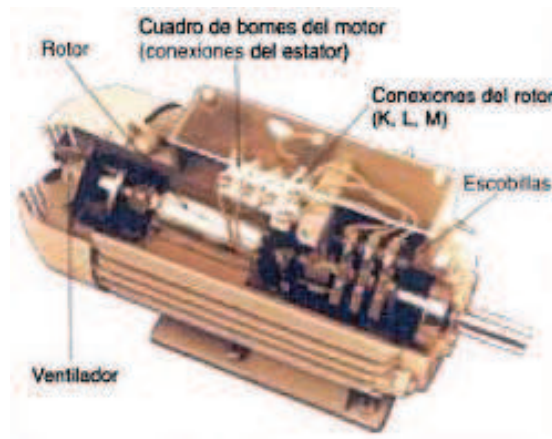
Corte motor trifásico asíncrono c.a. rotor bobinado
